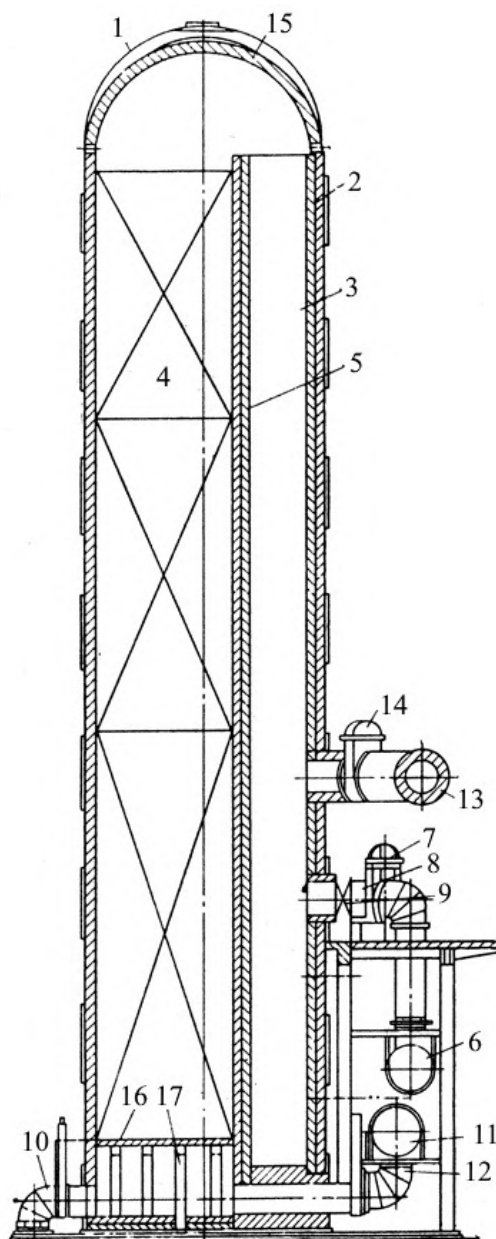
Устройство воздухонагревателя [6]:
